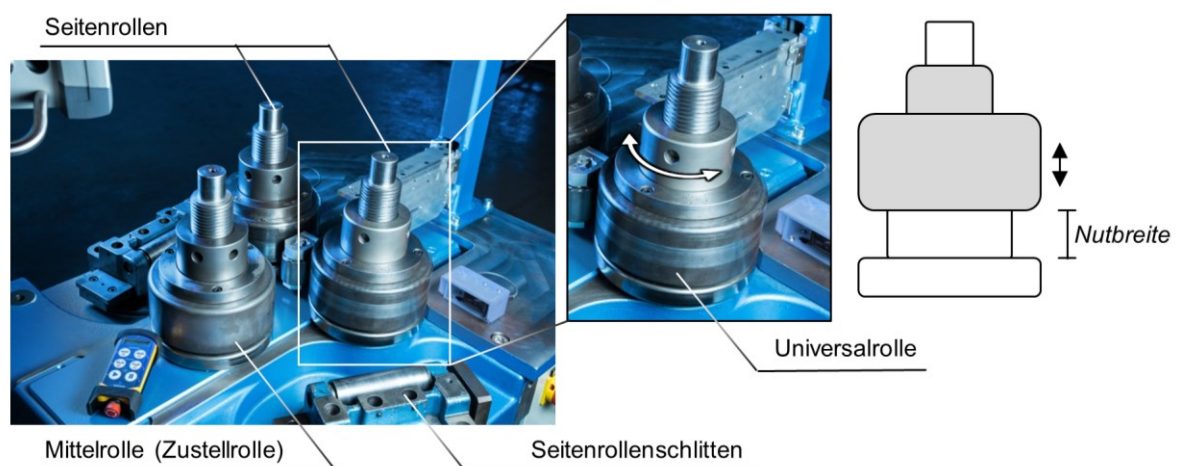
Drei-Rollen-Biegemaschine BO229 mit Universalrollensatz
